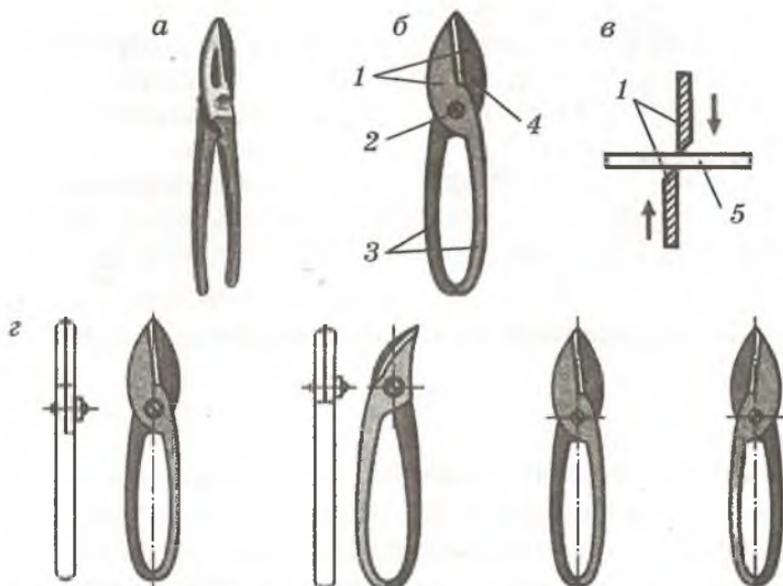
Ручные ножницы: а — общий вид; б — устройство ножниц: 1 — ножи, 2 — ось, 3 — ручки; 4 — лезвие, 5 — заготовка; в — схема резки; з — виды ручных ножниц: с прямыми, кривыми лезвиями, левые и правые
